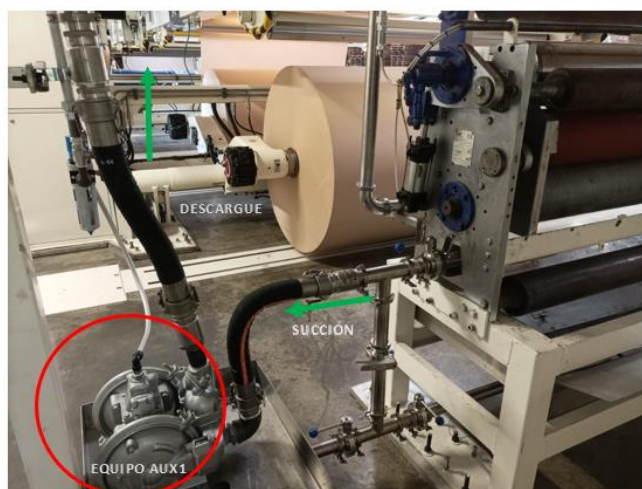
Instalación tubería de succión y descargue en equipo auxiliar 1 con conexión a bandeja de adhesivo. Fuente: Autor.
